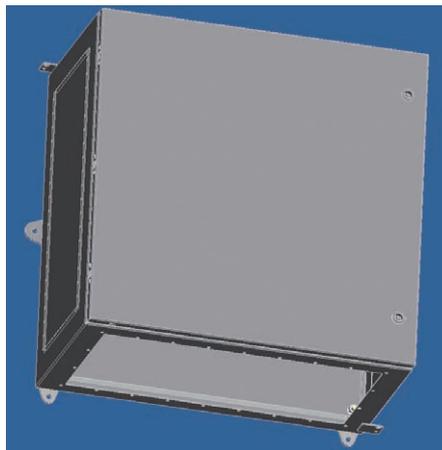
Вид корпуса навесного КН-2 в параметрической модели
